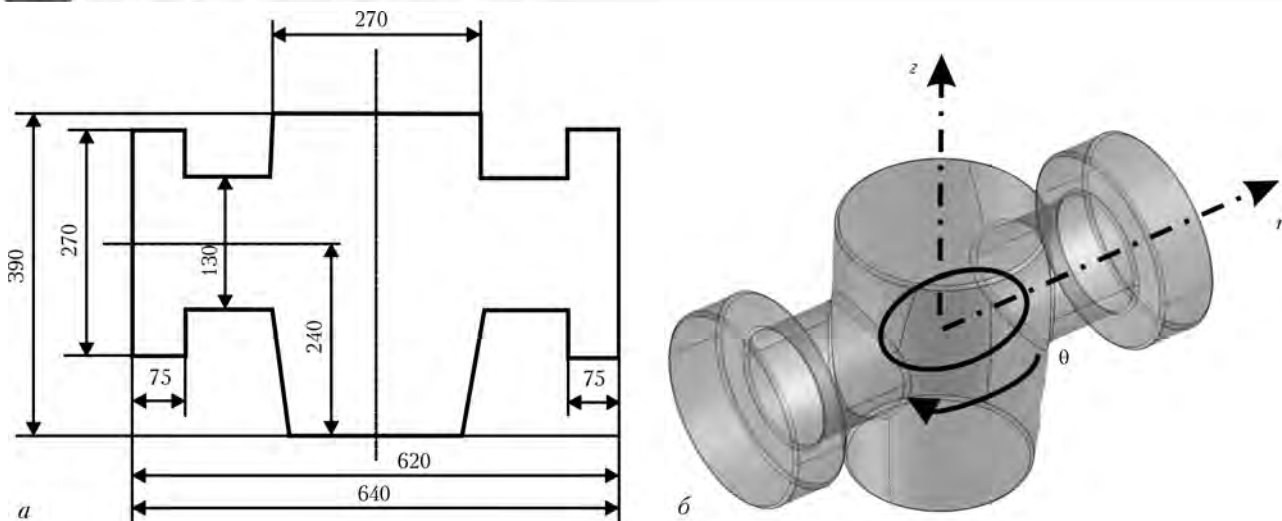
Заготовка корпуса фланцевой задвижки с условным проходом 80 мм: а — эскиз; б — изометрия
